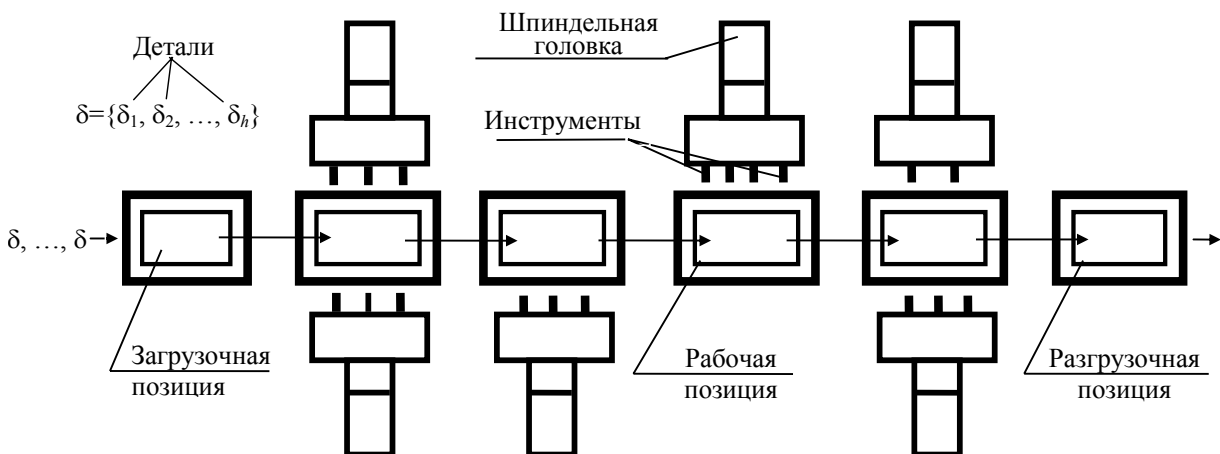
Общий вид конвейерной линии для групповой обработки деталей
